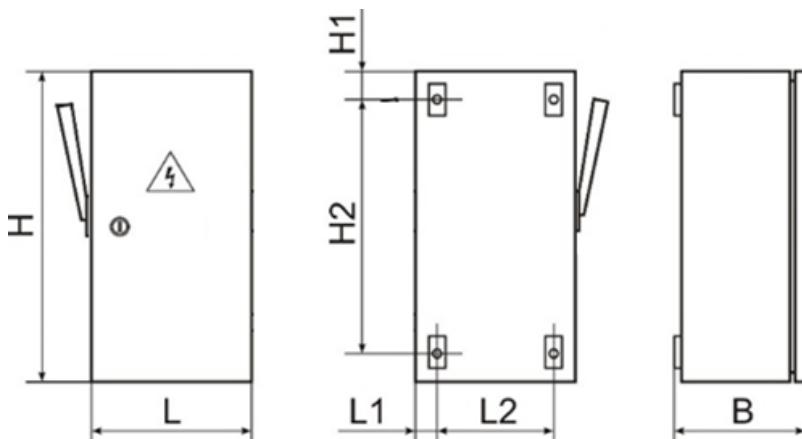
Общий вид и габаритные размеры ящиков силовых ЯРПП
